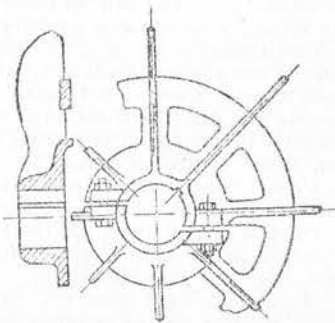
Ventilator centrifug, din aluminiu turnat.
